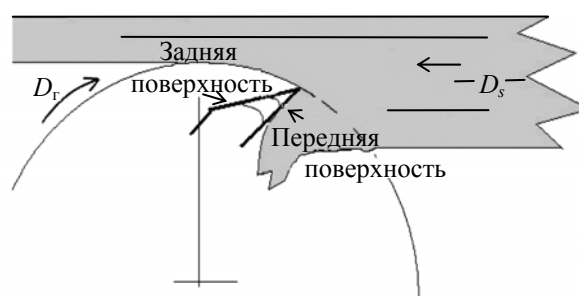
Схема взаимодействия режущего элемента фрезы с обрабатываемым материалом
